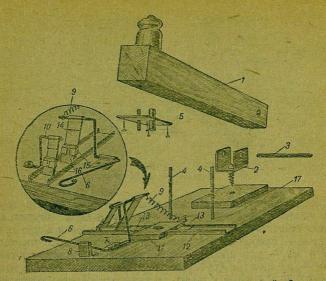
Перфоратор: I—рычаг пробойника отверстий, 2—подшипник, 3—ось рычага, 4—ограничивающие шпильки, 5—железная пластинка с пробойными трубками, 6—педаль, 7— шарнир педали, 8—ограничитель педали, 9—оттяжная пружина, 10— ось тормозной пластинки, 11—свинцовая плашка, 12—направляющий желобок, 13—козырьки, 14—подающая пластинка, 15—скобка, 16—резинки, 17—основание перфоратора.
